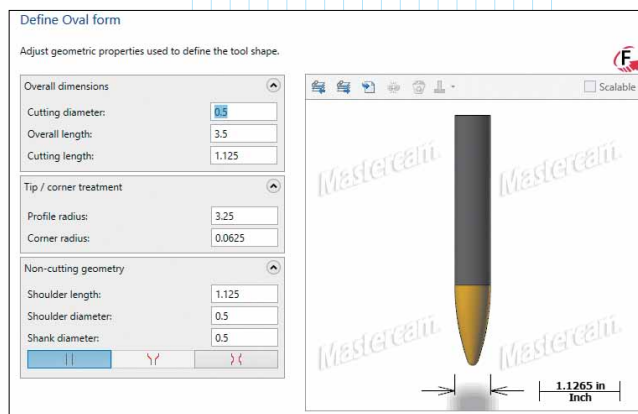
Новые типы инструмента – фрезы овального профиля и линзообразной боковой формы
